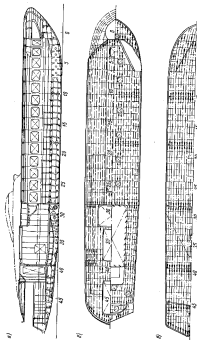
Конструктивная схема корпуса и надстройки теплохода «Росток»: а — внешний вид; б — план сечения; в — план палубы.
